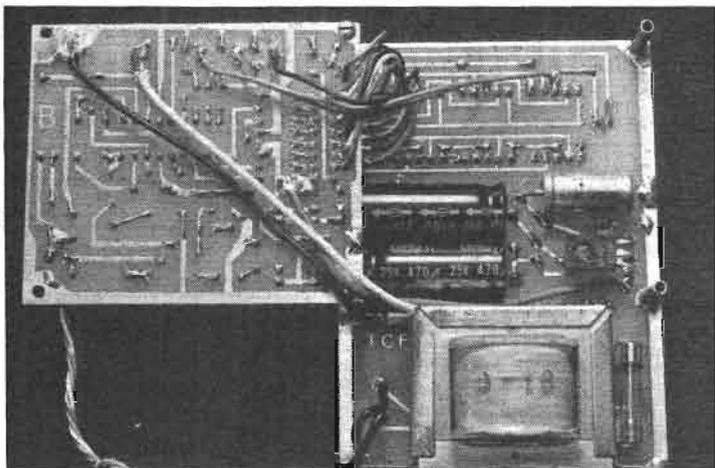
Photo E. – Disposition des deux platines pendant la pose des fils souples d'interconnexion. Noter les points de soudure des trois fils d'alimentation sur B.
